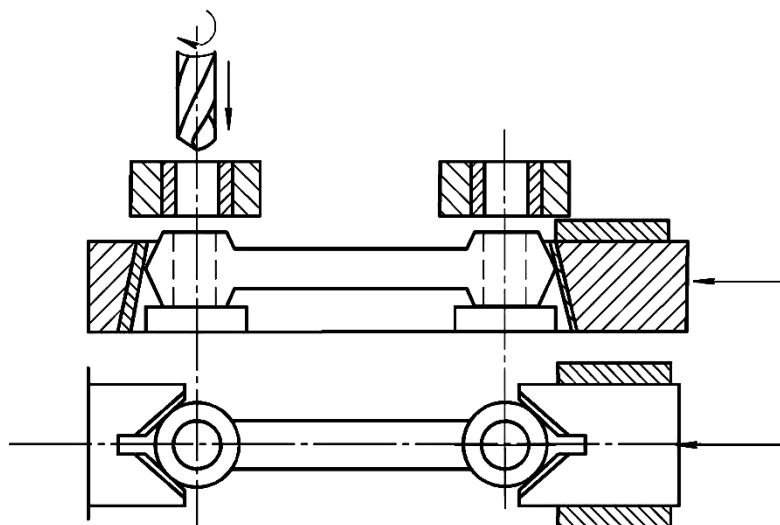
Схема пристосування для одночасного свердління отворів
